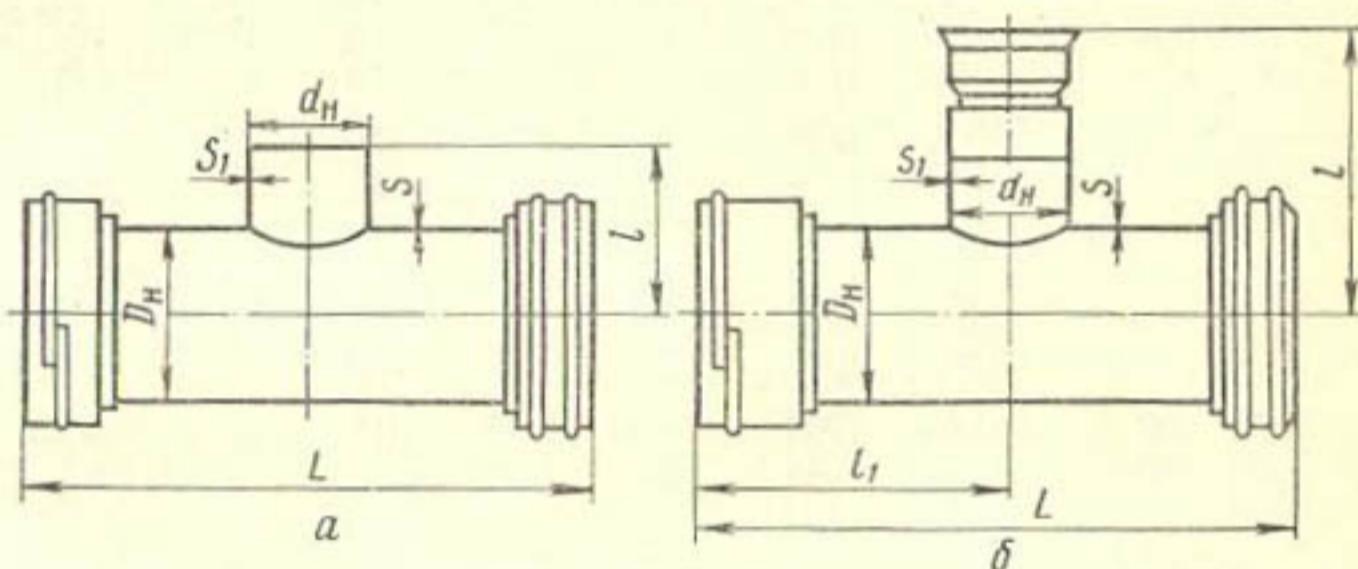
Тройники для соединения железобетонных труб с металлическими, асбестоцементными и пластмассовыми.
